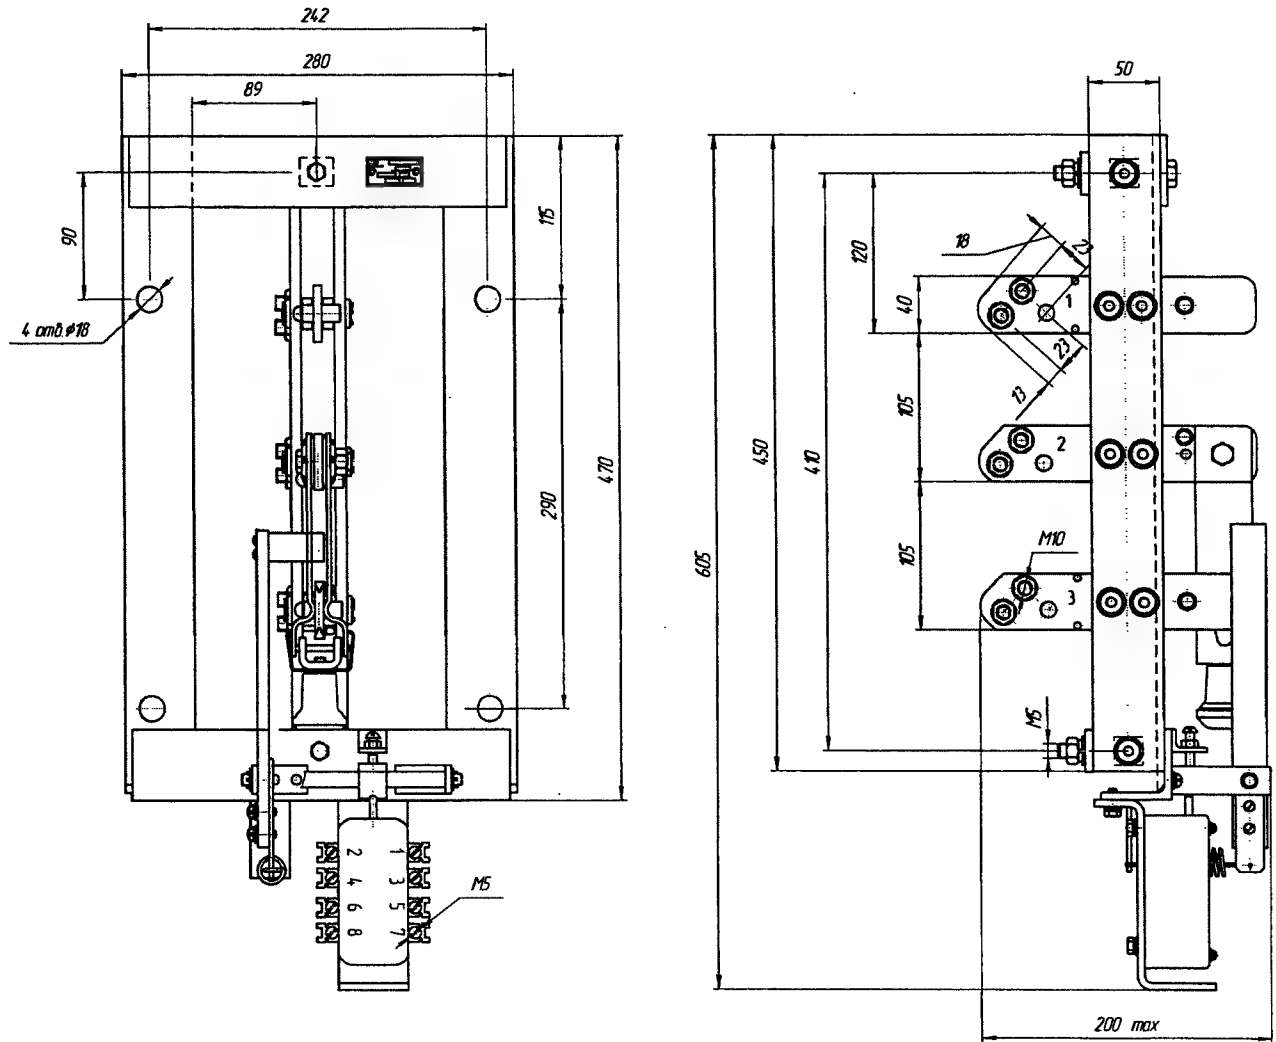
Габаритные, присоединительные и установочные размеры
